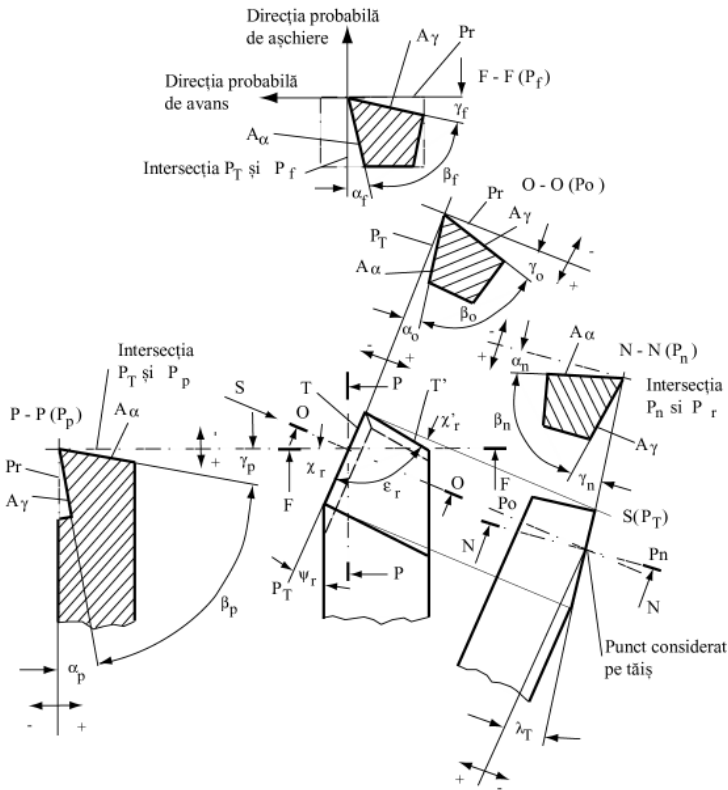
Geometria constructivă a cuțitului simplu de strung
